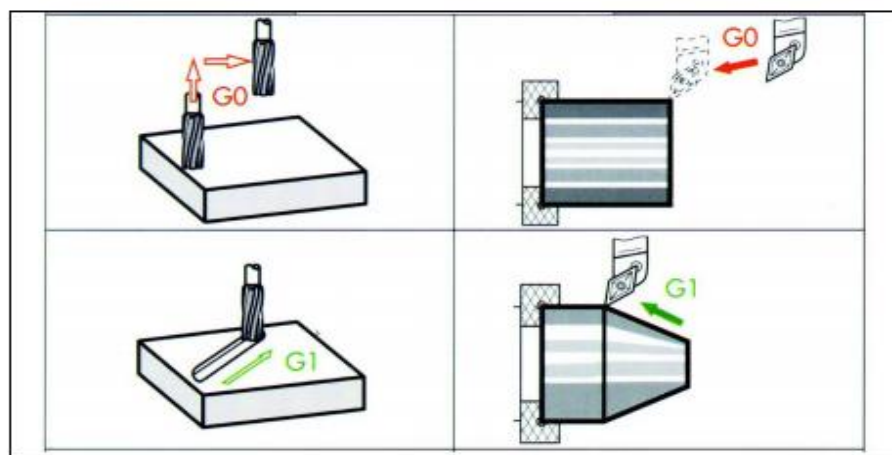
Déplacement G00 et G01 en cas de fraisage et tournage [3].
